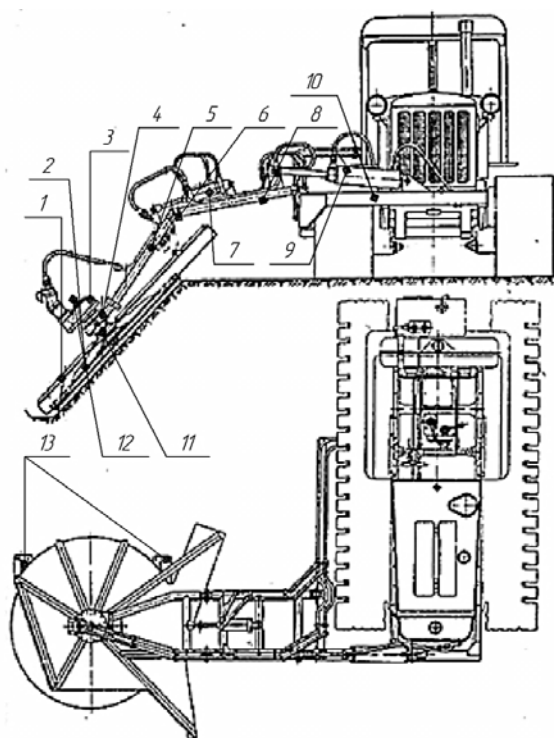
Однороторная механическая косилка: 1 – кожух; 2 – ротор (диск); 3 – гидромотор; 4 – разъемный сферический подшипник; 5 – рама рабочего органа; 6 – шарнир; 7, 9 – гидроцилиндры; 8 – поворотная рама; 10 – основная рама; 11 – корпус; 12 – ось рабочего органа; 13 – лыжа
